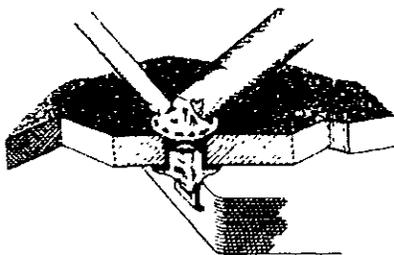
Después de pasar, se añade un poco más de soldadura para amontonarla otra vez.
